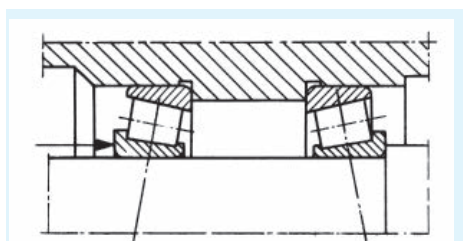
Wciskanie pierścienia wewnętrznego łożyska stożkowego
